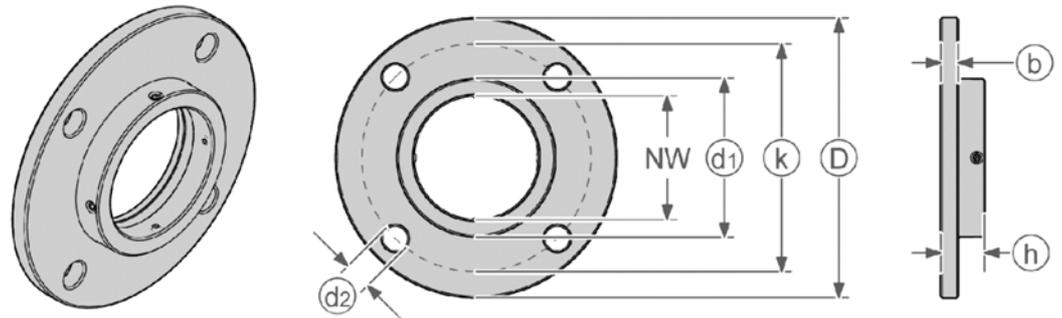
Dimensiones de la brida deslizable del quemador de ignición GFI
